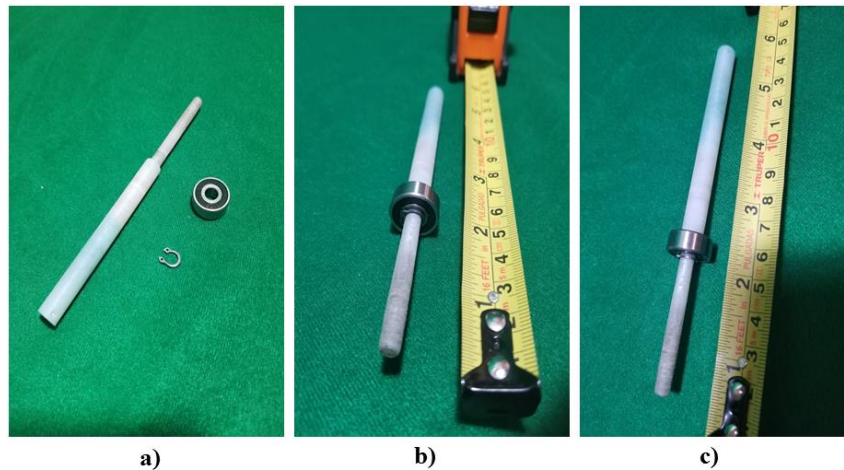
a) partes del eje principal del mezclador, b) Ensamble del eje principal de agitador vista frontal, c) Ensamble del eje principal de agitador vista superior.
